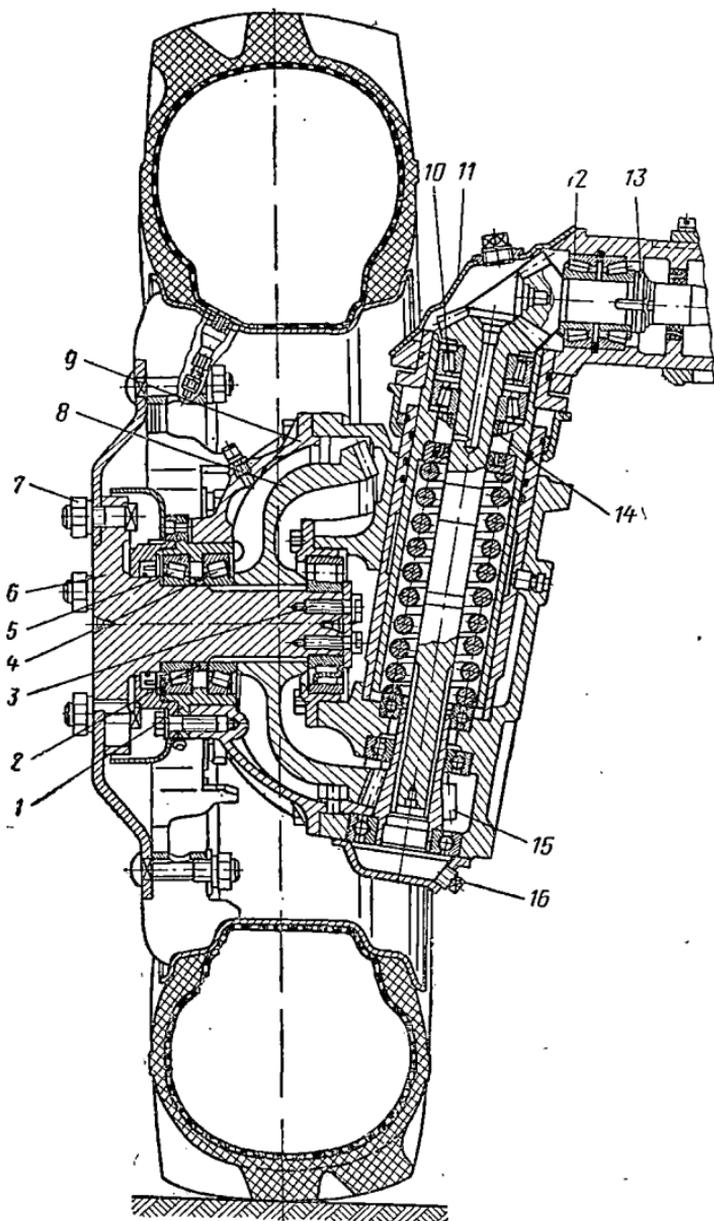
Колесный редуктор переднего ведущего моста тракторов МТЗ-82 и МТЗ-82Л:
